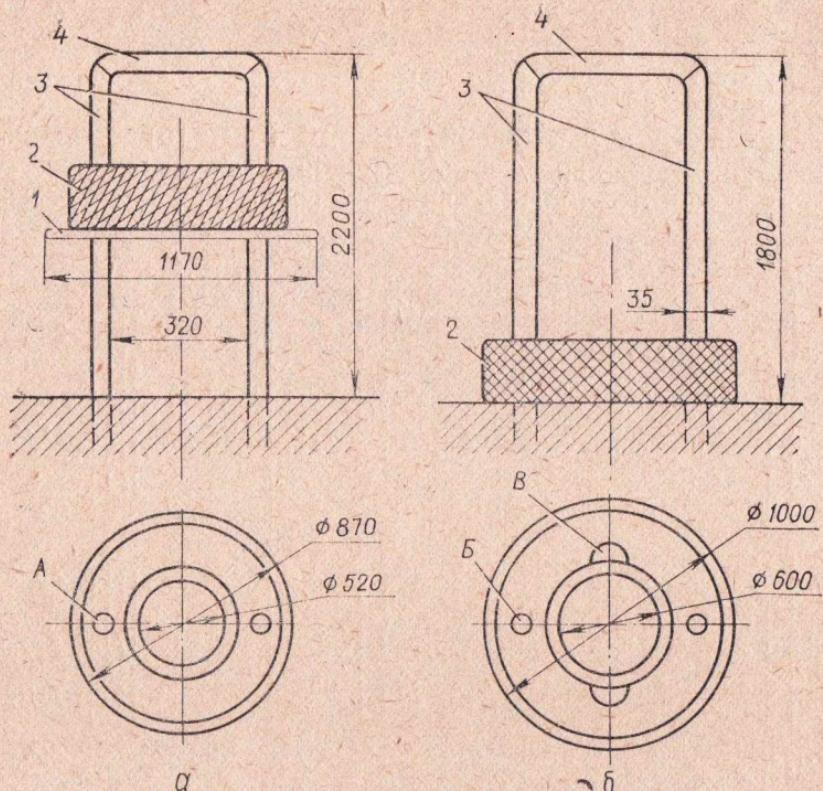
Тренажеры (*а* и *б*) для силовой подготовки:
